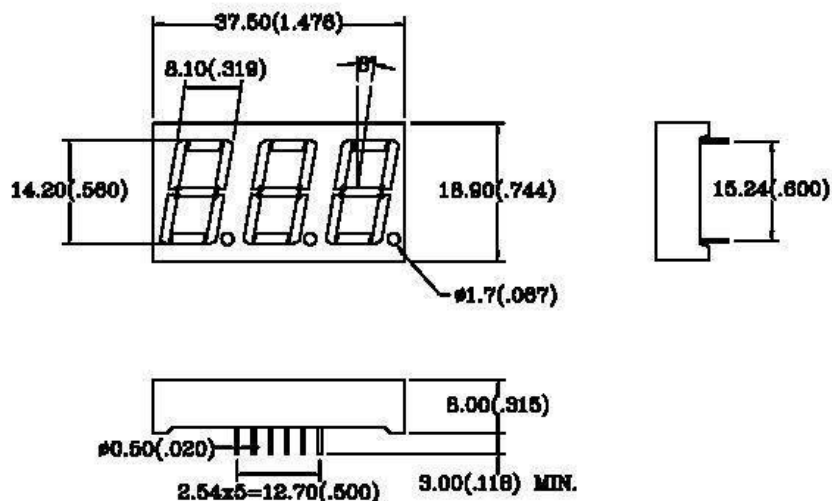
Габаритні розміри індикатора BC56-12EWA "Kingbright"
